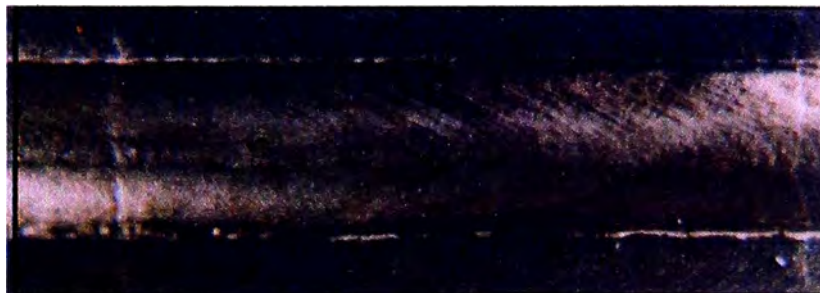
Fisuras en la soldadura transversales que aparecen en una soldadura de arco protegida por gas multipase en una unión soldada de acero de alta resistencia.
